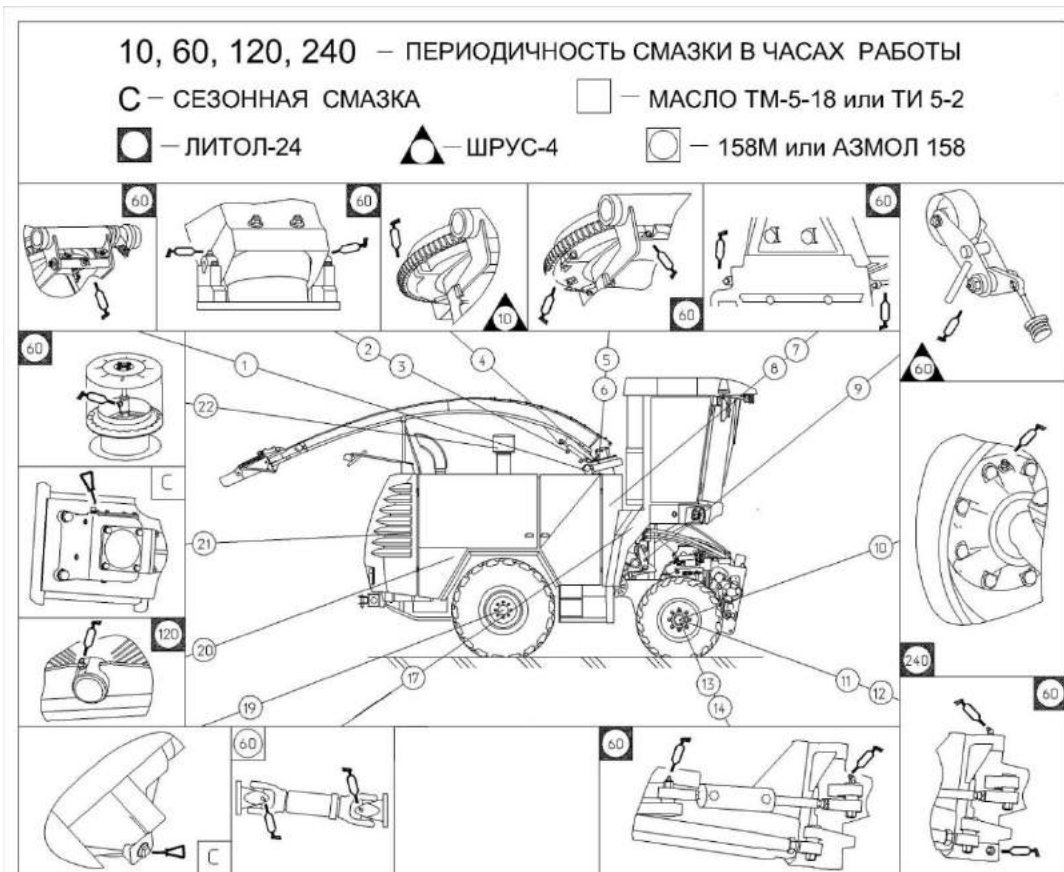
Схема смазки самоходного измельчителя (вид справа)
